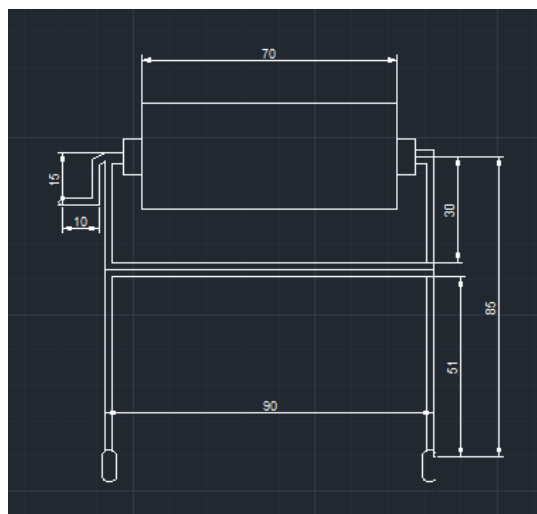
Ilustração do protótipo da bobina com manivela (medidas em cm)
